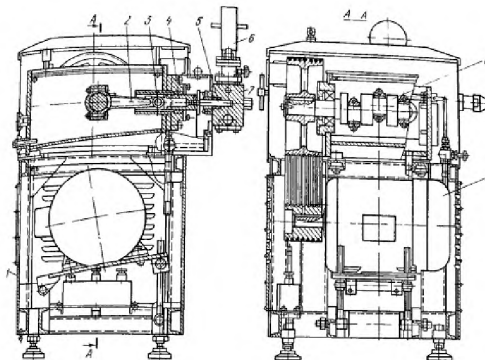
Конструкція гомогенізатора К5 – ОГА –1,2 (1 – станина; 2 – кривошипно-шатунний механізм; 3 – палець; 4 – повзун; 5 – плунжер; 6 – манометрична головка; 7 – блок плунжерний; 8 – колінчастий вал; 9 – електродвигун.)
